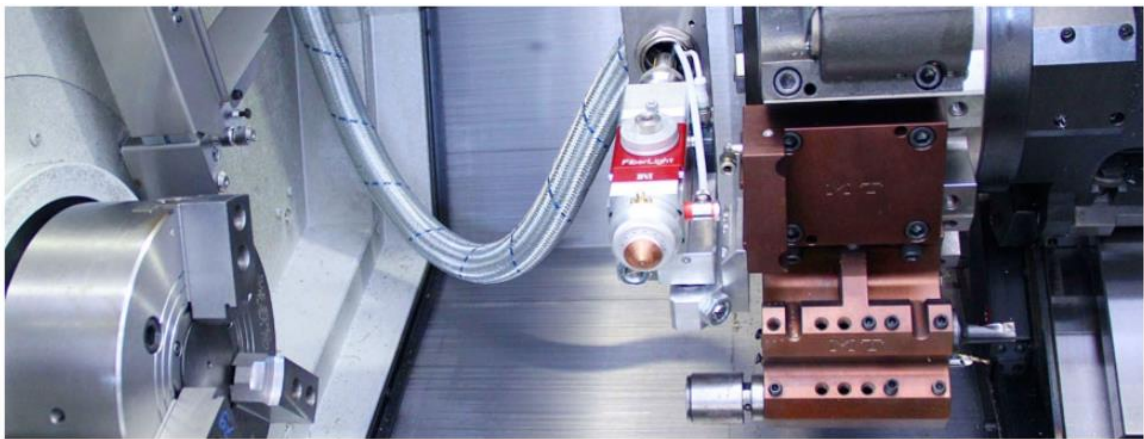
Пристрій для лазерного різання на верстаті з револьвером
